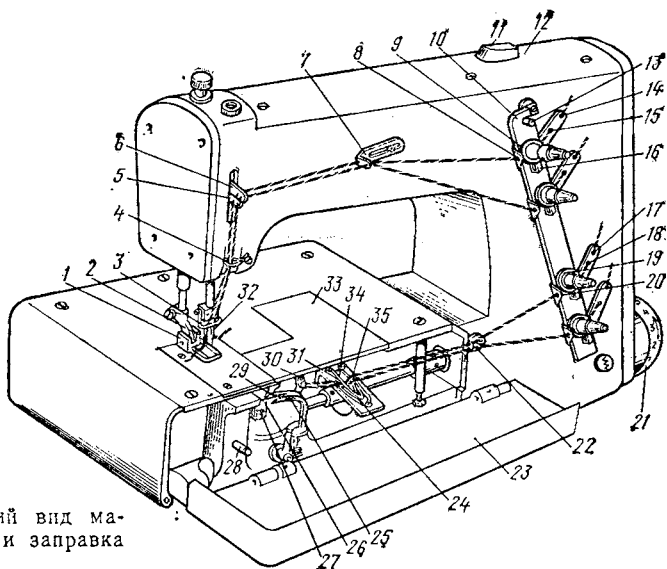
Внешний вид машины 976-I кл. и заправка ниток
